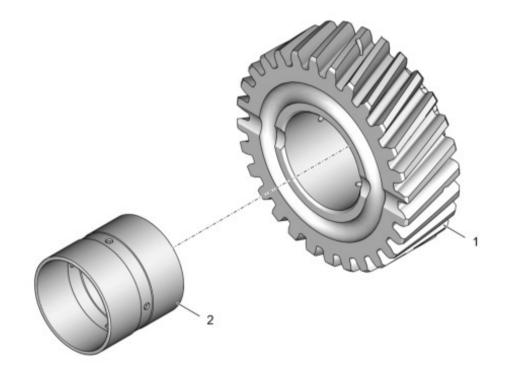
4322-1802034 Шестерня высшей передачи первичного вала
